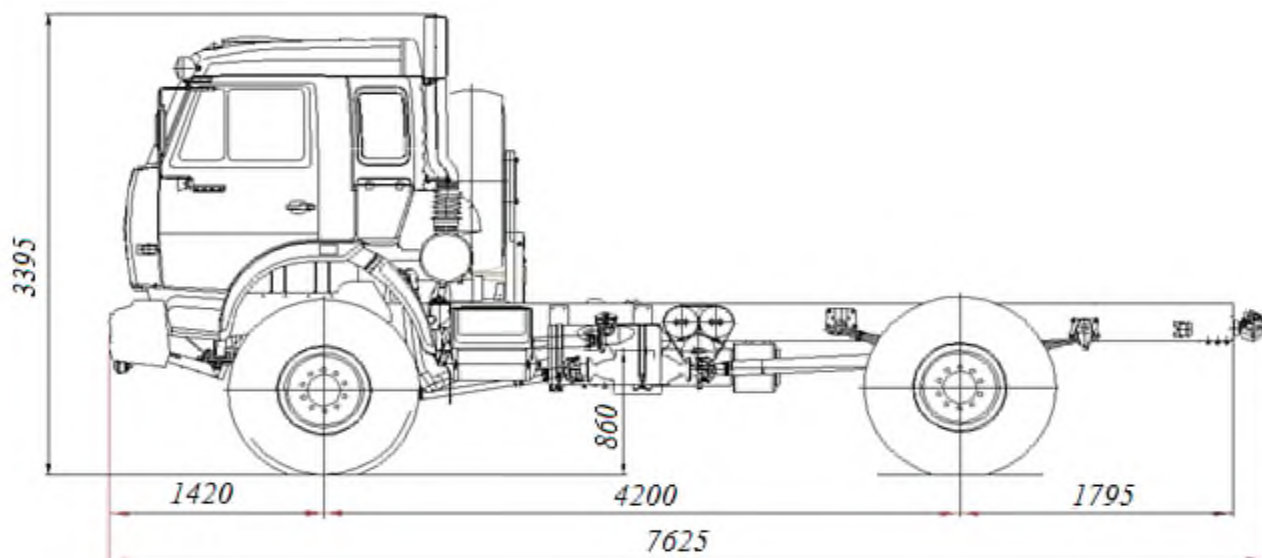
Внешний вид автомобиля КАМАЗ-4326
